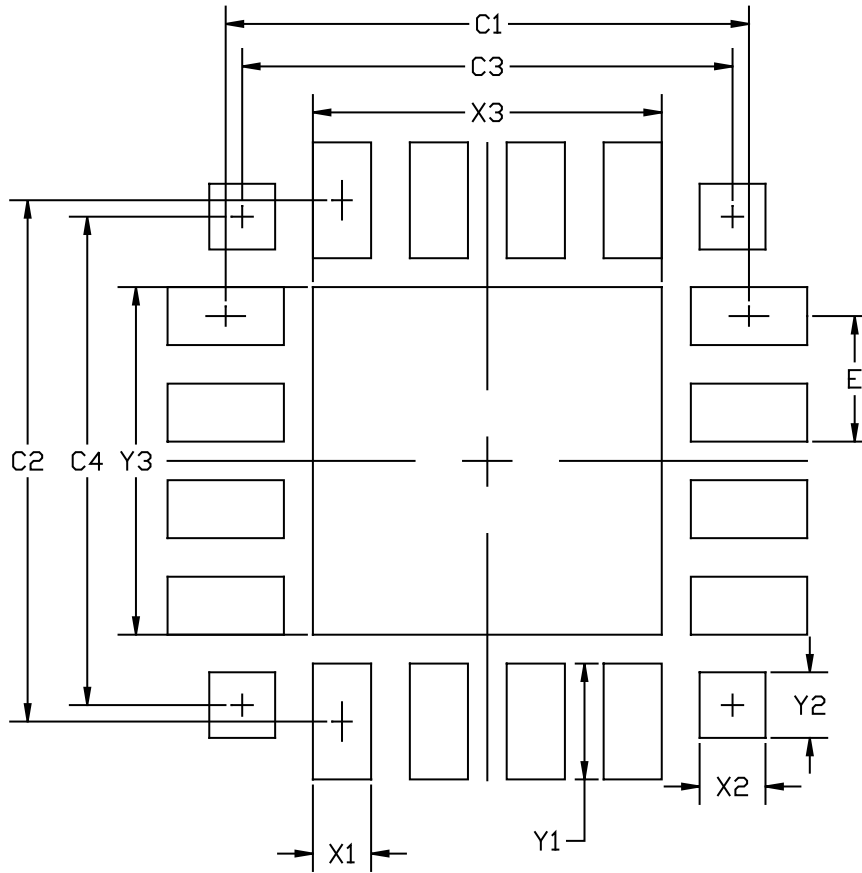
QFN20 PCB 焊盘布局图
